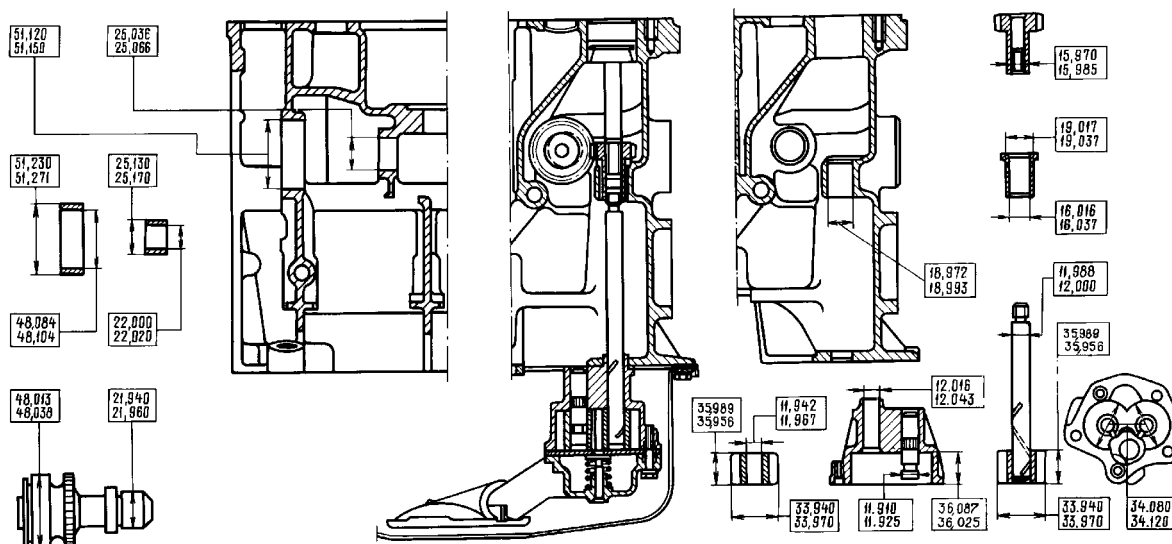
Основные размеры деталей масляного насоса и его привода.
